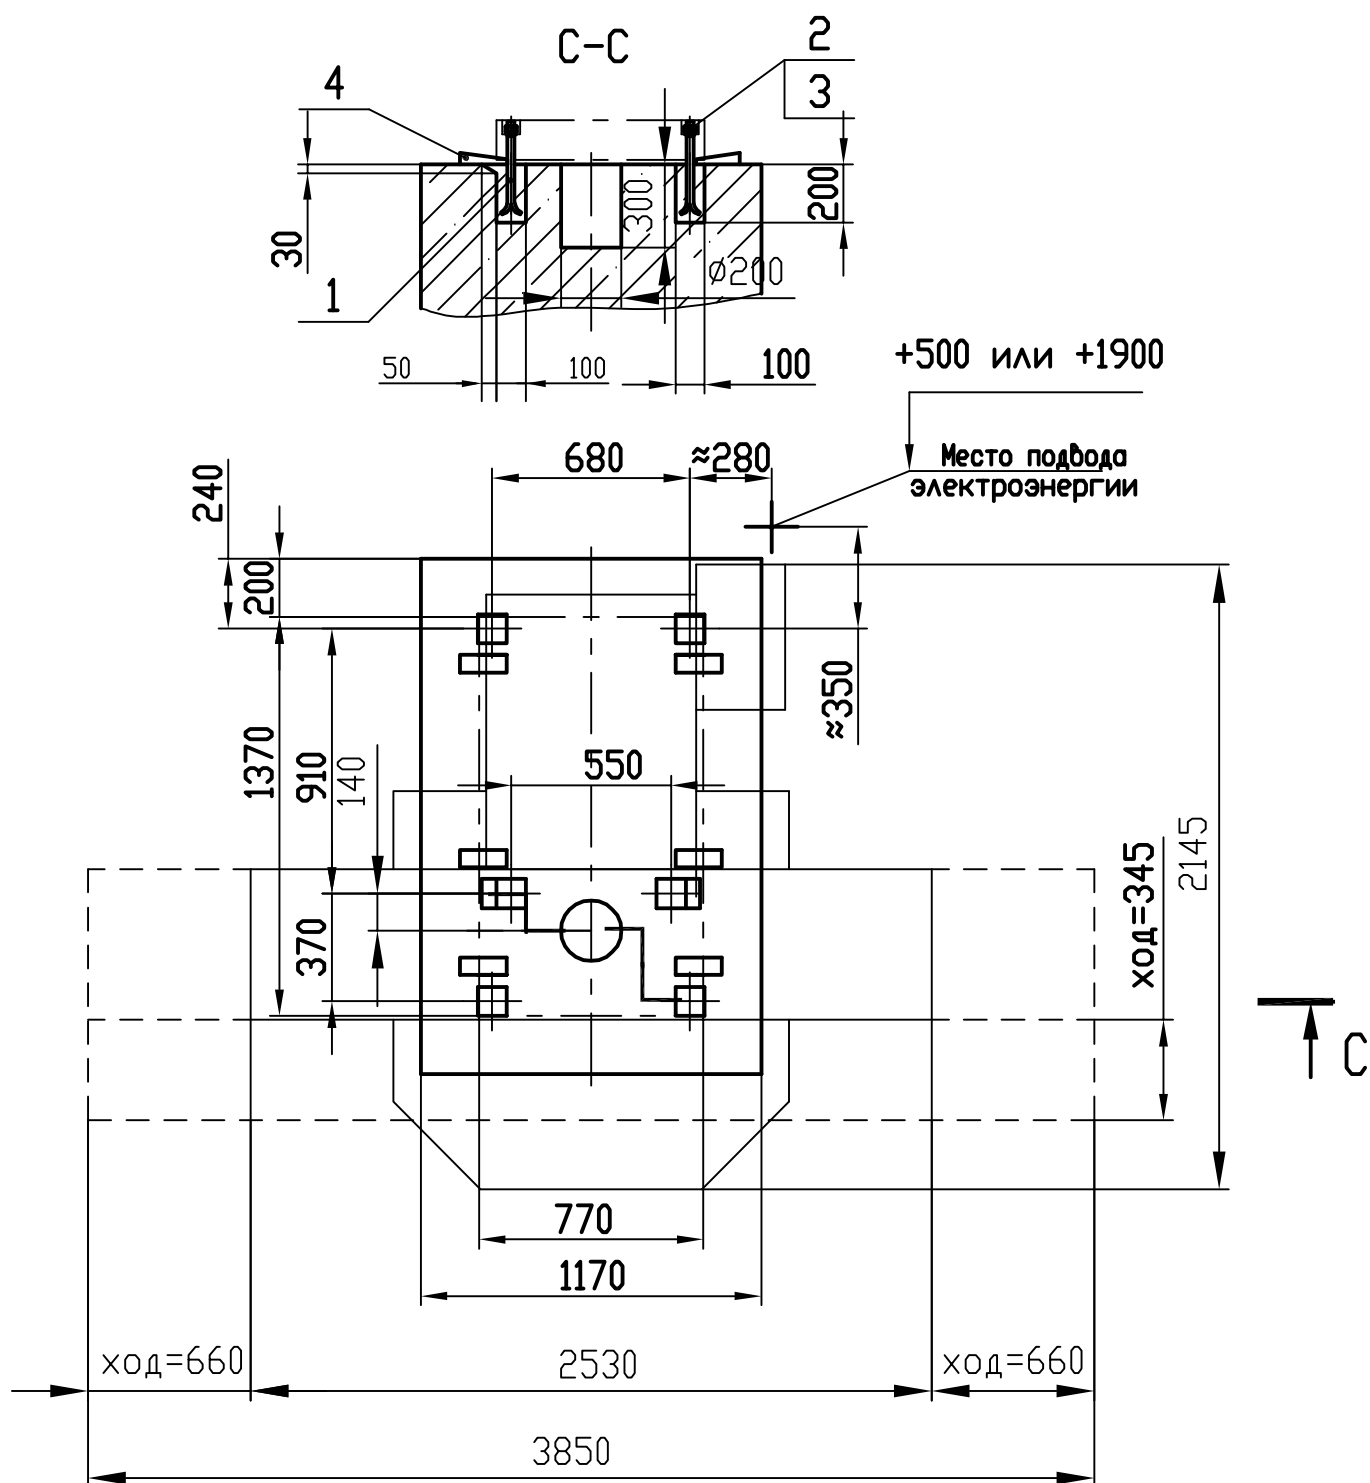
Монтажный чертеж для станка FSS450MR-01,
